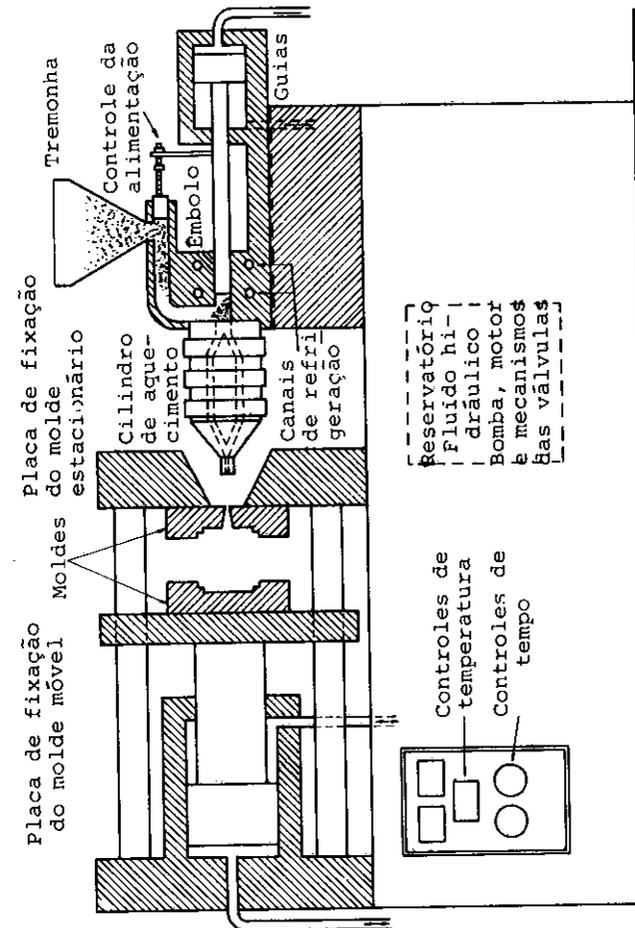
Máquina de moldagem por injeção de êmbolo simples.
